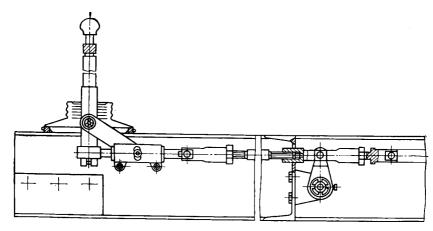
Управление коробки передач агрегата Азинмаш-32М
